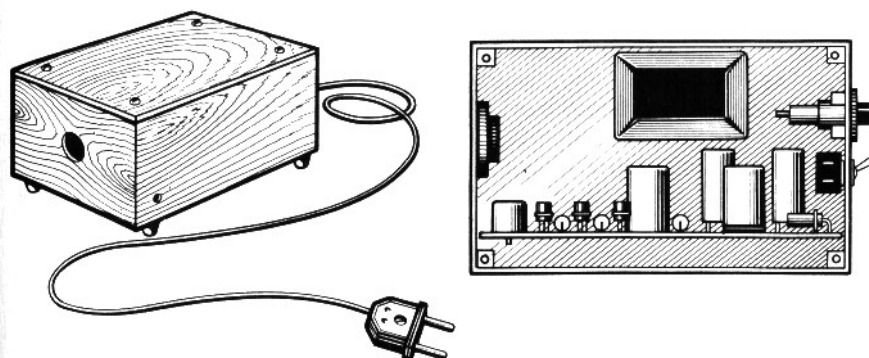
Внешний вид автомата и размещение деталей внутри корпуса
